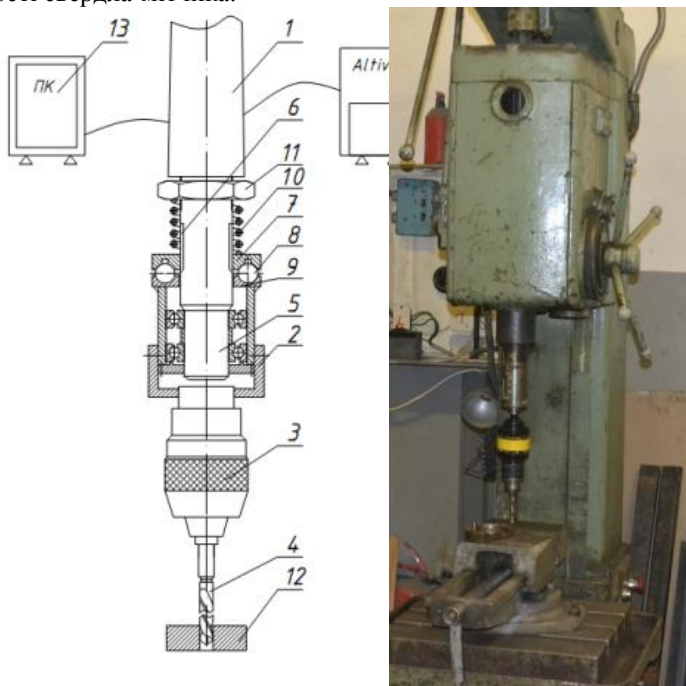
Конструкція пристрою для дослідження стійкості свердла-мітчика: а) конструктивна схема; б) загальний вигляд
